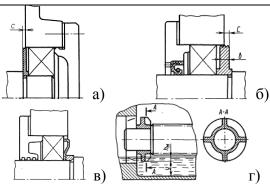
Внутренняя защита подшипника: а) МЗШ — Маслозащитная шайба; б) МУШ — Мазеудерживающая шайба; в) УП — уплотнительная шайба; г) Бр - брызговик
